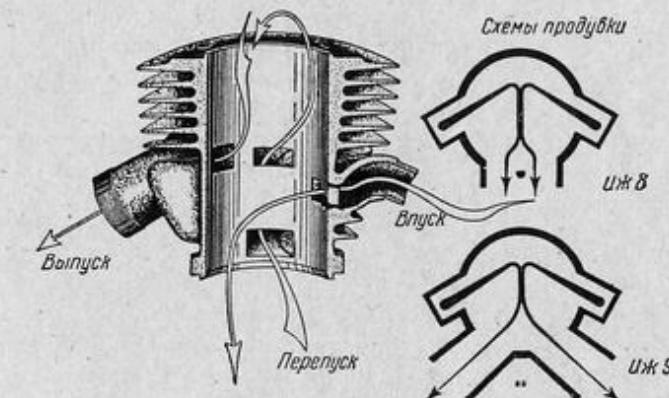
Цилиндр двигателя ИЖ-9 и схемы продувки ИЖ-8 и ИЖ-9.
